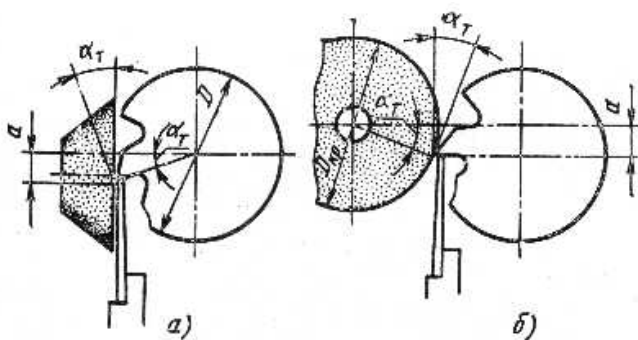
Схема установки круга при заточке задней поверхности инструмента:
